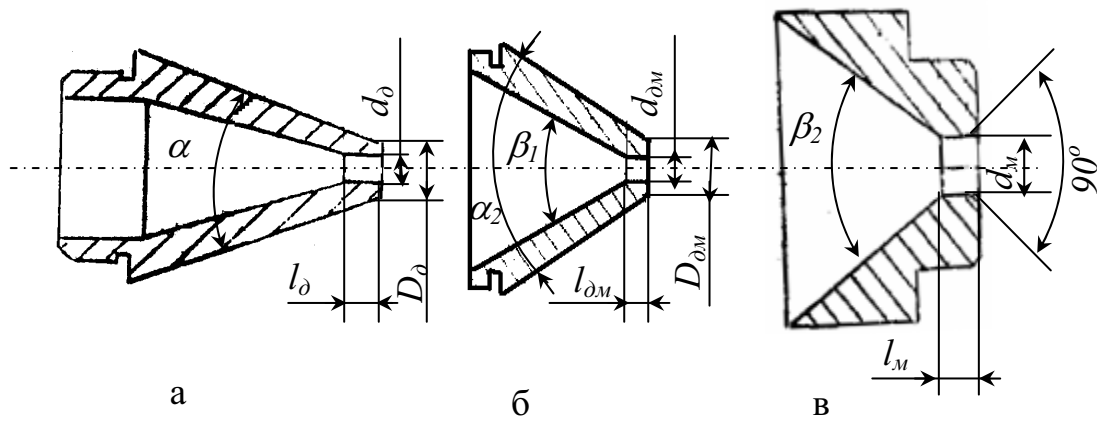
Формующий инструмент для двухслойного наложения изоляции и экрана или изоляции и оболочки: а – дорн; б – матрица-дорн; в – матрица
